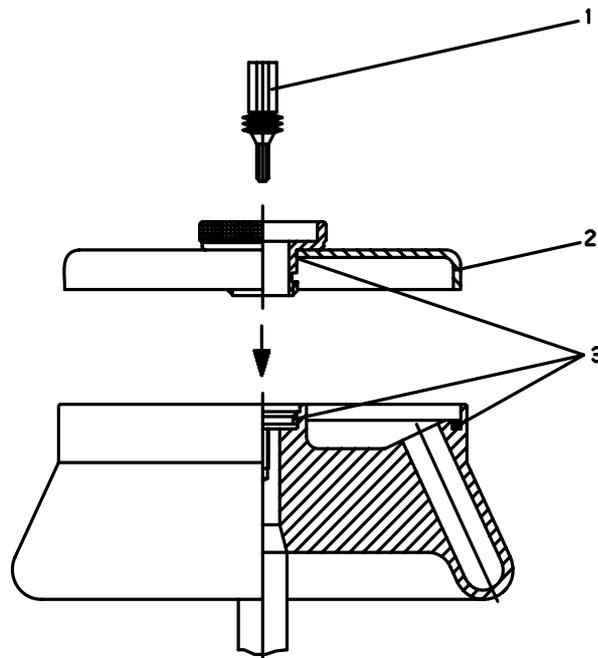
Rotor angulaire avec couvercle hermétique
